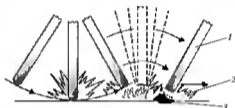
Возбуждение дуги и начало формирования сварного шва:
